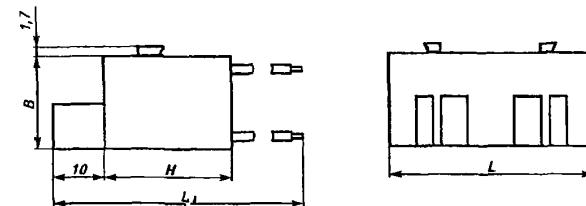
Габаритные и установочные размеры ограничителя перенапряжений типа ОПН 1
